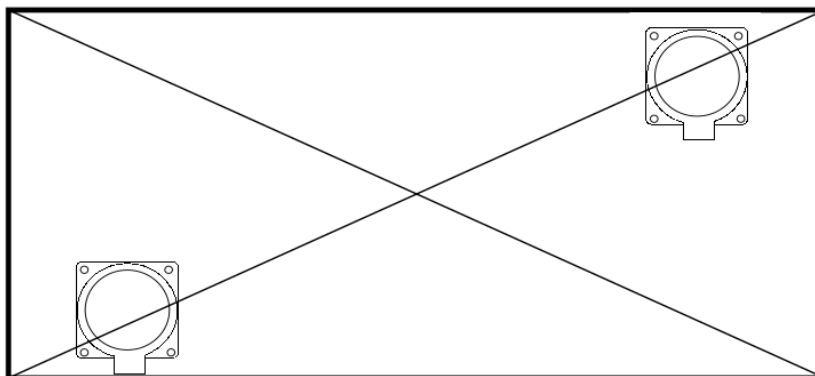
Установка двух ДУТ в топливный бак – вид сверху
